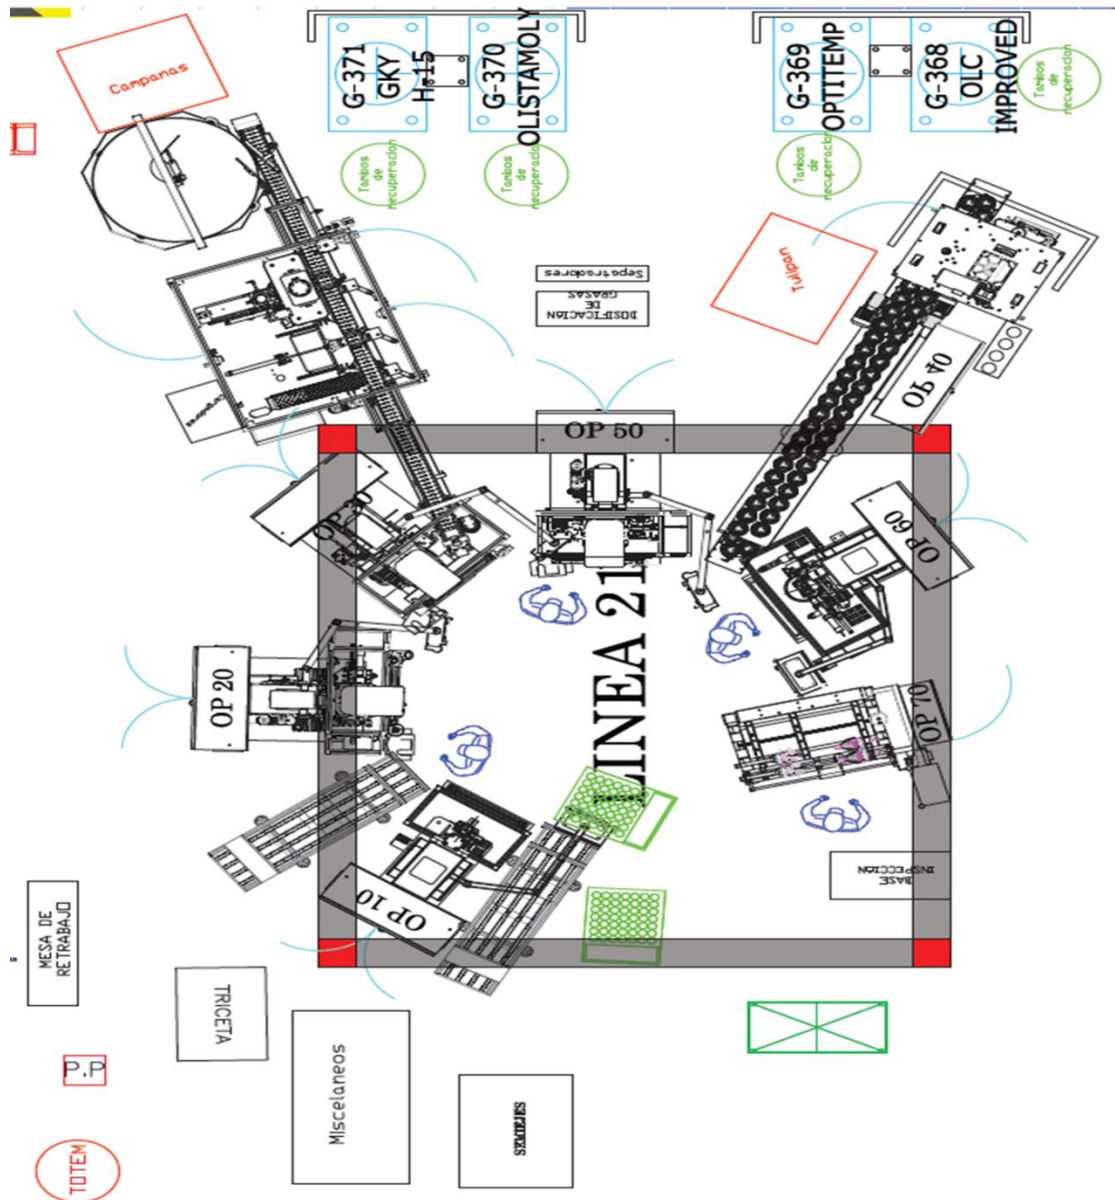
, Lay out de la línea 21, Fuente: Archivos de manufactura
